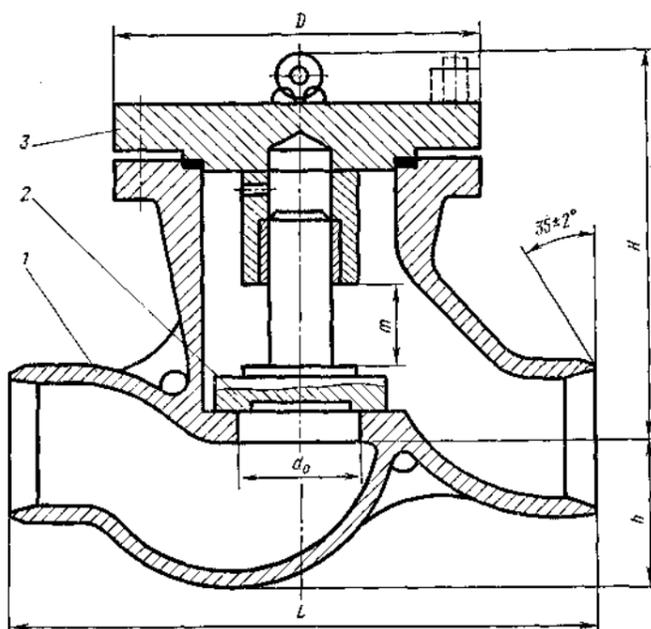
Обратный клапан подъемный T-186 и T-1186
